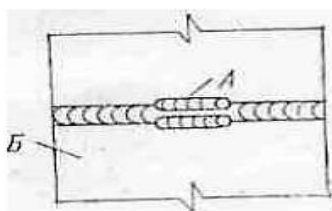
Многократная наварка А на участок сварного соединения и лист стенки Б резервуара в дефектном месте
